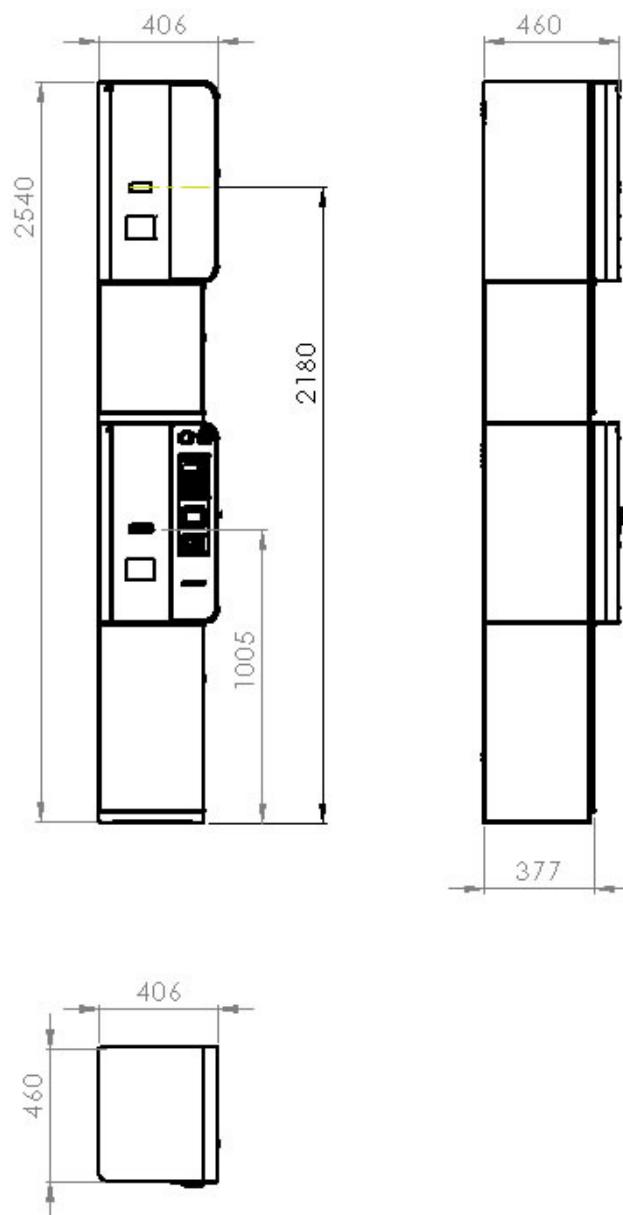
IN/OUT TwinDeck, dimensions en mm
